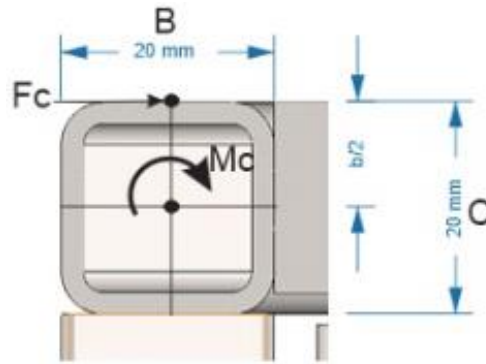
Vista de corte en tubo de soporte mecanismo leva cilíndrica.
